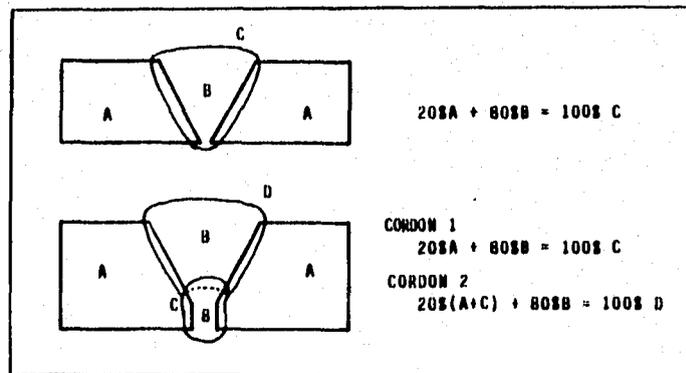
DILUCION EN CORDONES DE SOLDADURA.
